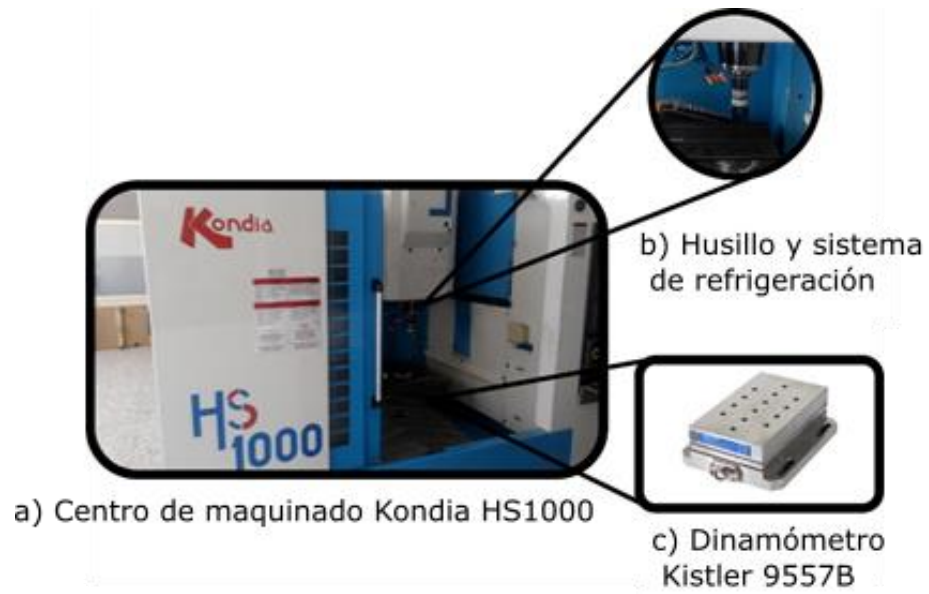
Centro universal de maquinado y equipamiento sensorial para la medición de fuerzas de corte.
